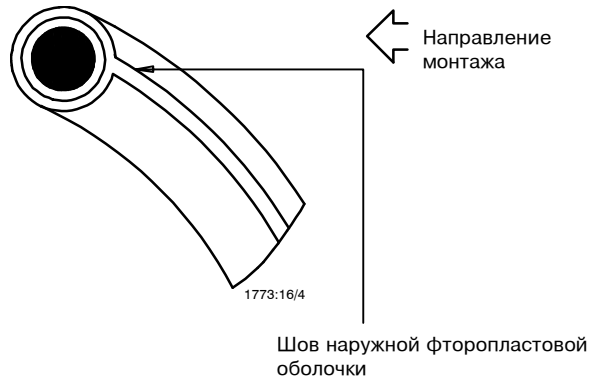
Прокладка круглого сечения с фторопластовой оболочкой
